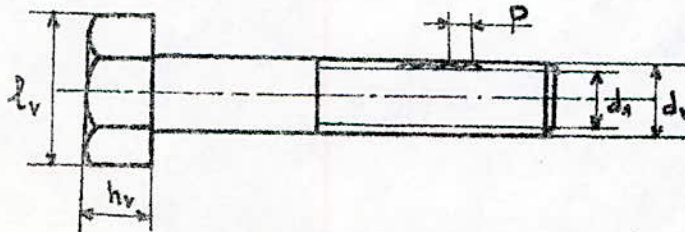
Vis d'assemblage du chapeau sur le corps de bielle
